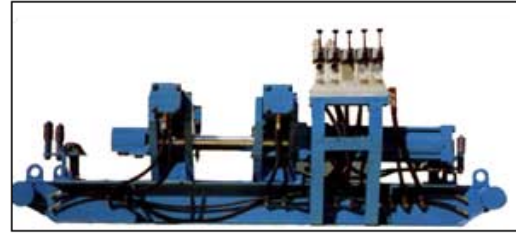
Общий вид установки для механического соединения труб [14]
